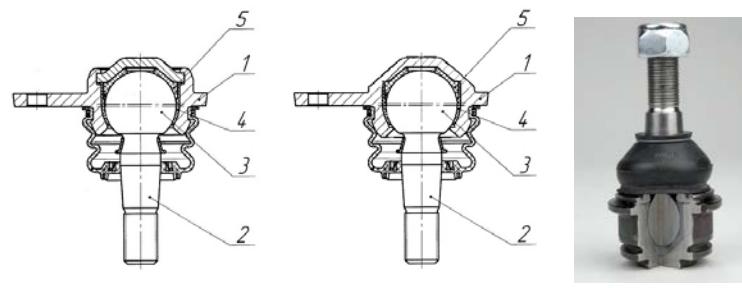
Неразборные шаровые опоры: а – с обжимом корпуса при сборке опоры сверху; б – с обжимом корпуса при сборке опоры снизу; 1 – корпус; 2 – палец; 3 – сферическая головка; 4 – пластмассовый «стакан»; 5 – пластмассовая опора; в – общий вид неразборной шаровой опоры [2]
